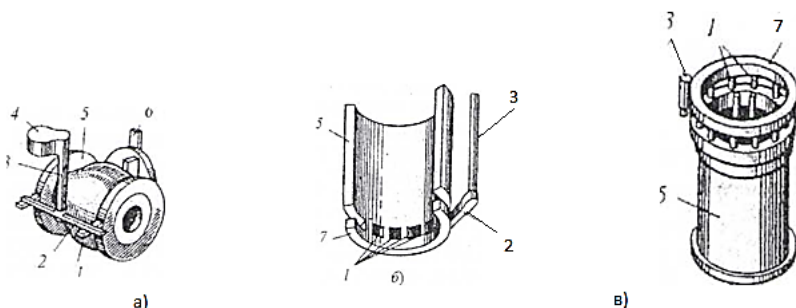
Способы подвода расплавленного металла в полость литейной формы
